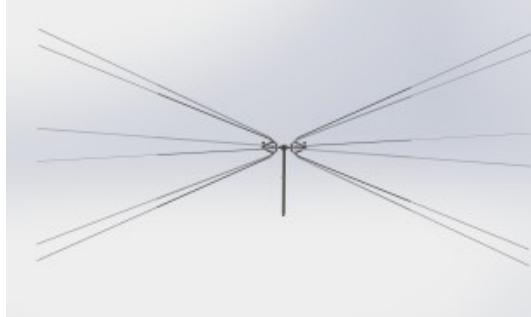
Balun + BBFA 9146 Elemente mit kleinem Öffnungswinkel und mit Extensions.
